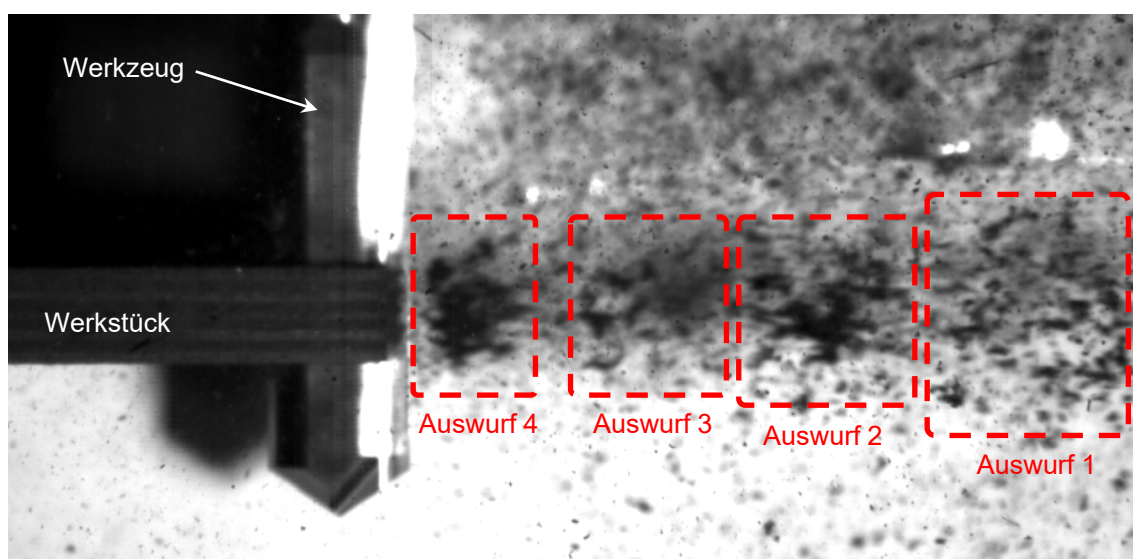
Stoßweiser Auswurf des Spanguts durch das Fräswerkzeug
